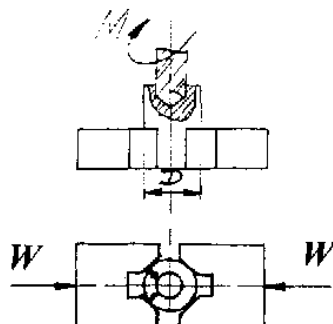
Затиск заготовки призмами при свердлінні
